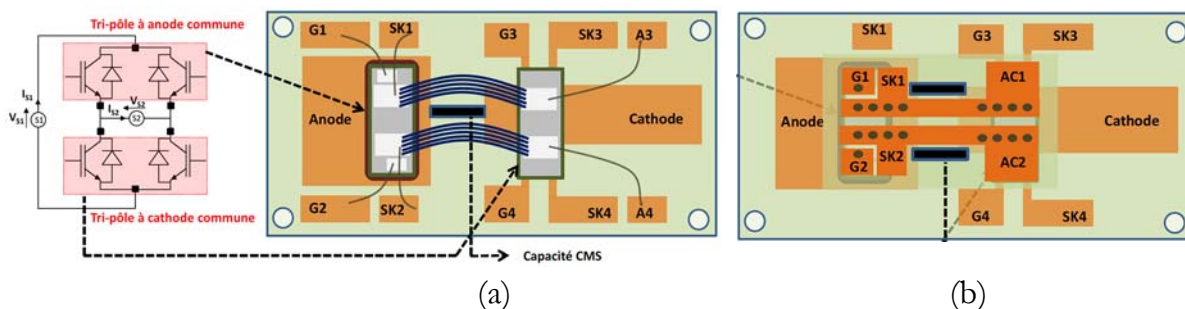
assemblage proposé pour le convertisseur bi-puce : (a) version à fils de *bonding* et (b) version à clip PCB [1]
